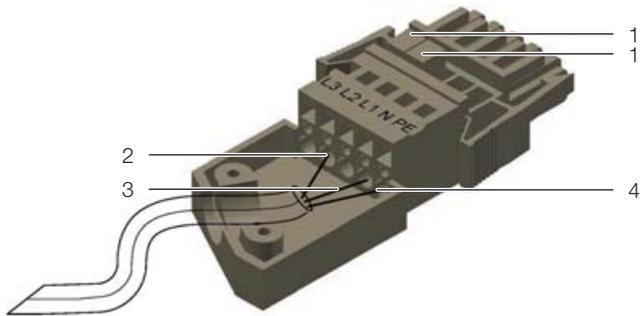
Schema des Anschlusssteckers mit Zugentlastungsgehäuse
